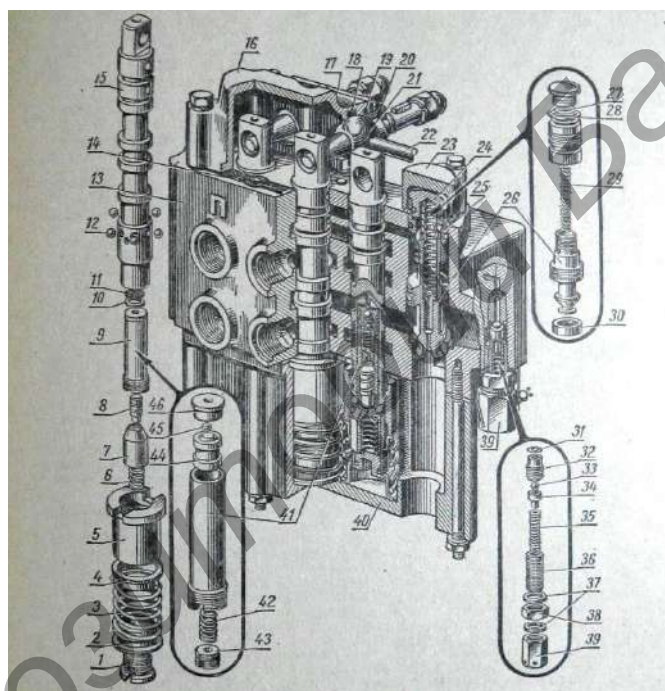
Распределитель Р75-ВЗ: 1-Пробка; 2-нижняя тарелка; 3-пружина автомат; 4-верхняя тарелка; 6-пружина втулки фиксатора; 7-втулка фиксатора; 8-бустер; 9, 41-гильзы; 10 и 14-прокладки; 11-фильтр; 12-шарик фиксатора; 13-корпус распределителя; 15-золотник; 16-верняя крышка; 17-планка; 18 и 27-уплотнительное кольцо; 19-пыльник; 20-пылезащитная манжета; 21-рычаг; 22-ось рычагов; 23-упор; 24-пробка перепускного клапана; 25-направляющая перепускного клапана; 26-перепускной клапан; 28-стопорное кольцо; 29-пружина перепускного клапана; 30-седло перепускного клапана; 31 и 37-уплотнительные шайбы; 32-гнездо предохранительного клапана; 33-шарик; 34-направляющая предохранительного клапана; 35-пружина предохранительного клапана; 36 и 43 регулировочные винты; 38-контргайка; 39-колпачок; 40 - нижняя крышка; 42 - пружина клапана автомата; 44-направляющая клапана автомата; 45-шариковый клапан; 46-гнездо клапана автомата
